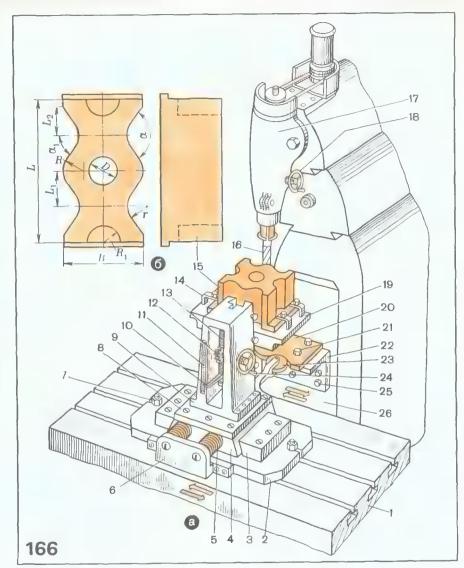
Обработка профиля пуансопо шаблон-копиру на универсальном приспособлении: приспособление и приемы фрезерования, б - деталь
